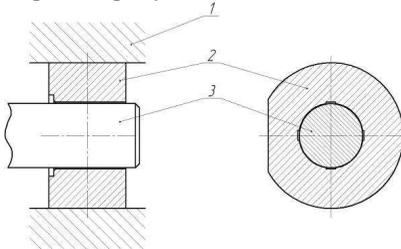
ГСДП1: 1 – корпус насоса; 2 – подшипник; 3 – цапфа вала
